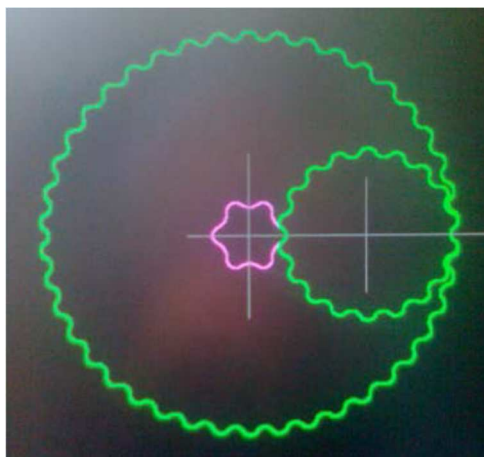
Планетарный редуктор с циклоидальным профилем зубьев (схема 6-18-42)
